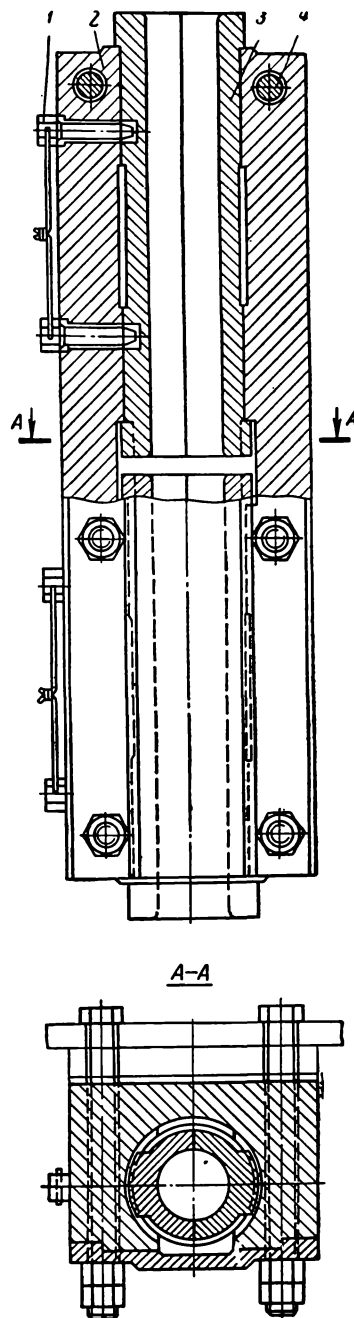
Общий вид конструкции направляющей втулки подъемного сосуда для канатных проводников: 1 — фиксирующие винты; 2 — разъемный корпус; 3 — сменные разъемные вкладыши; 4 — болты крепления
